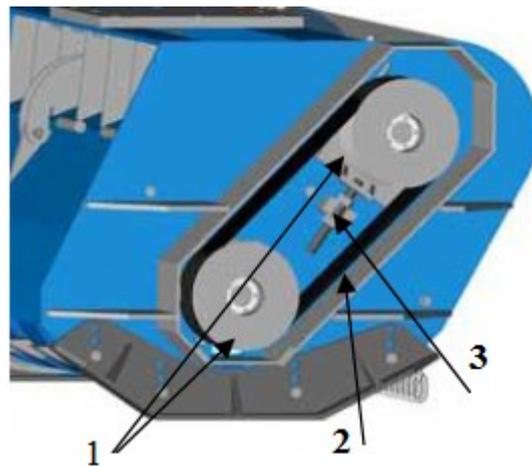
Реверсивный редуктор для привода ременной передачи мульчера
